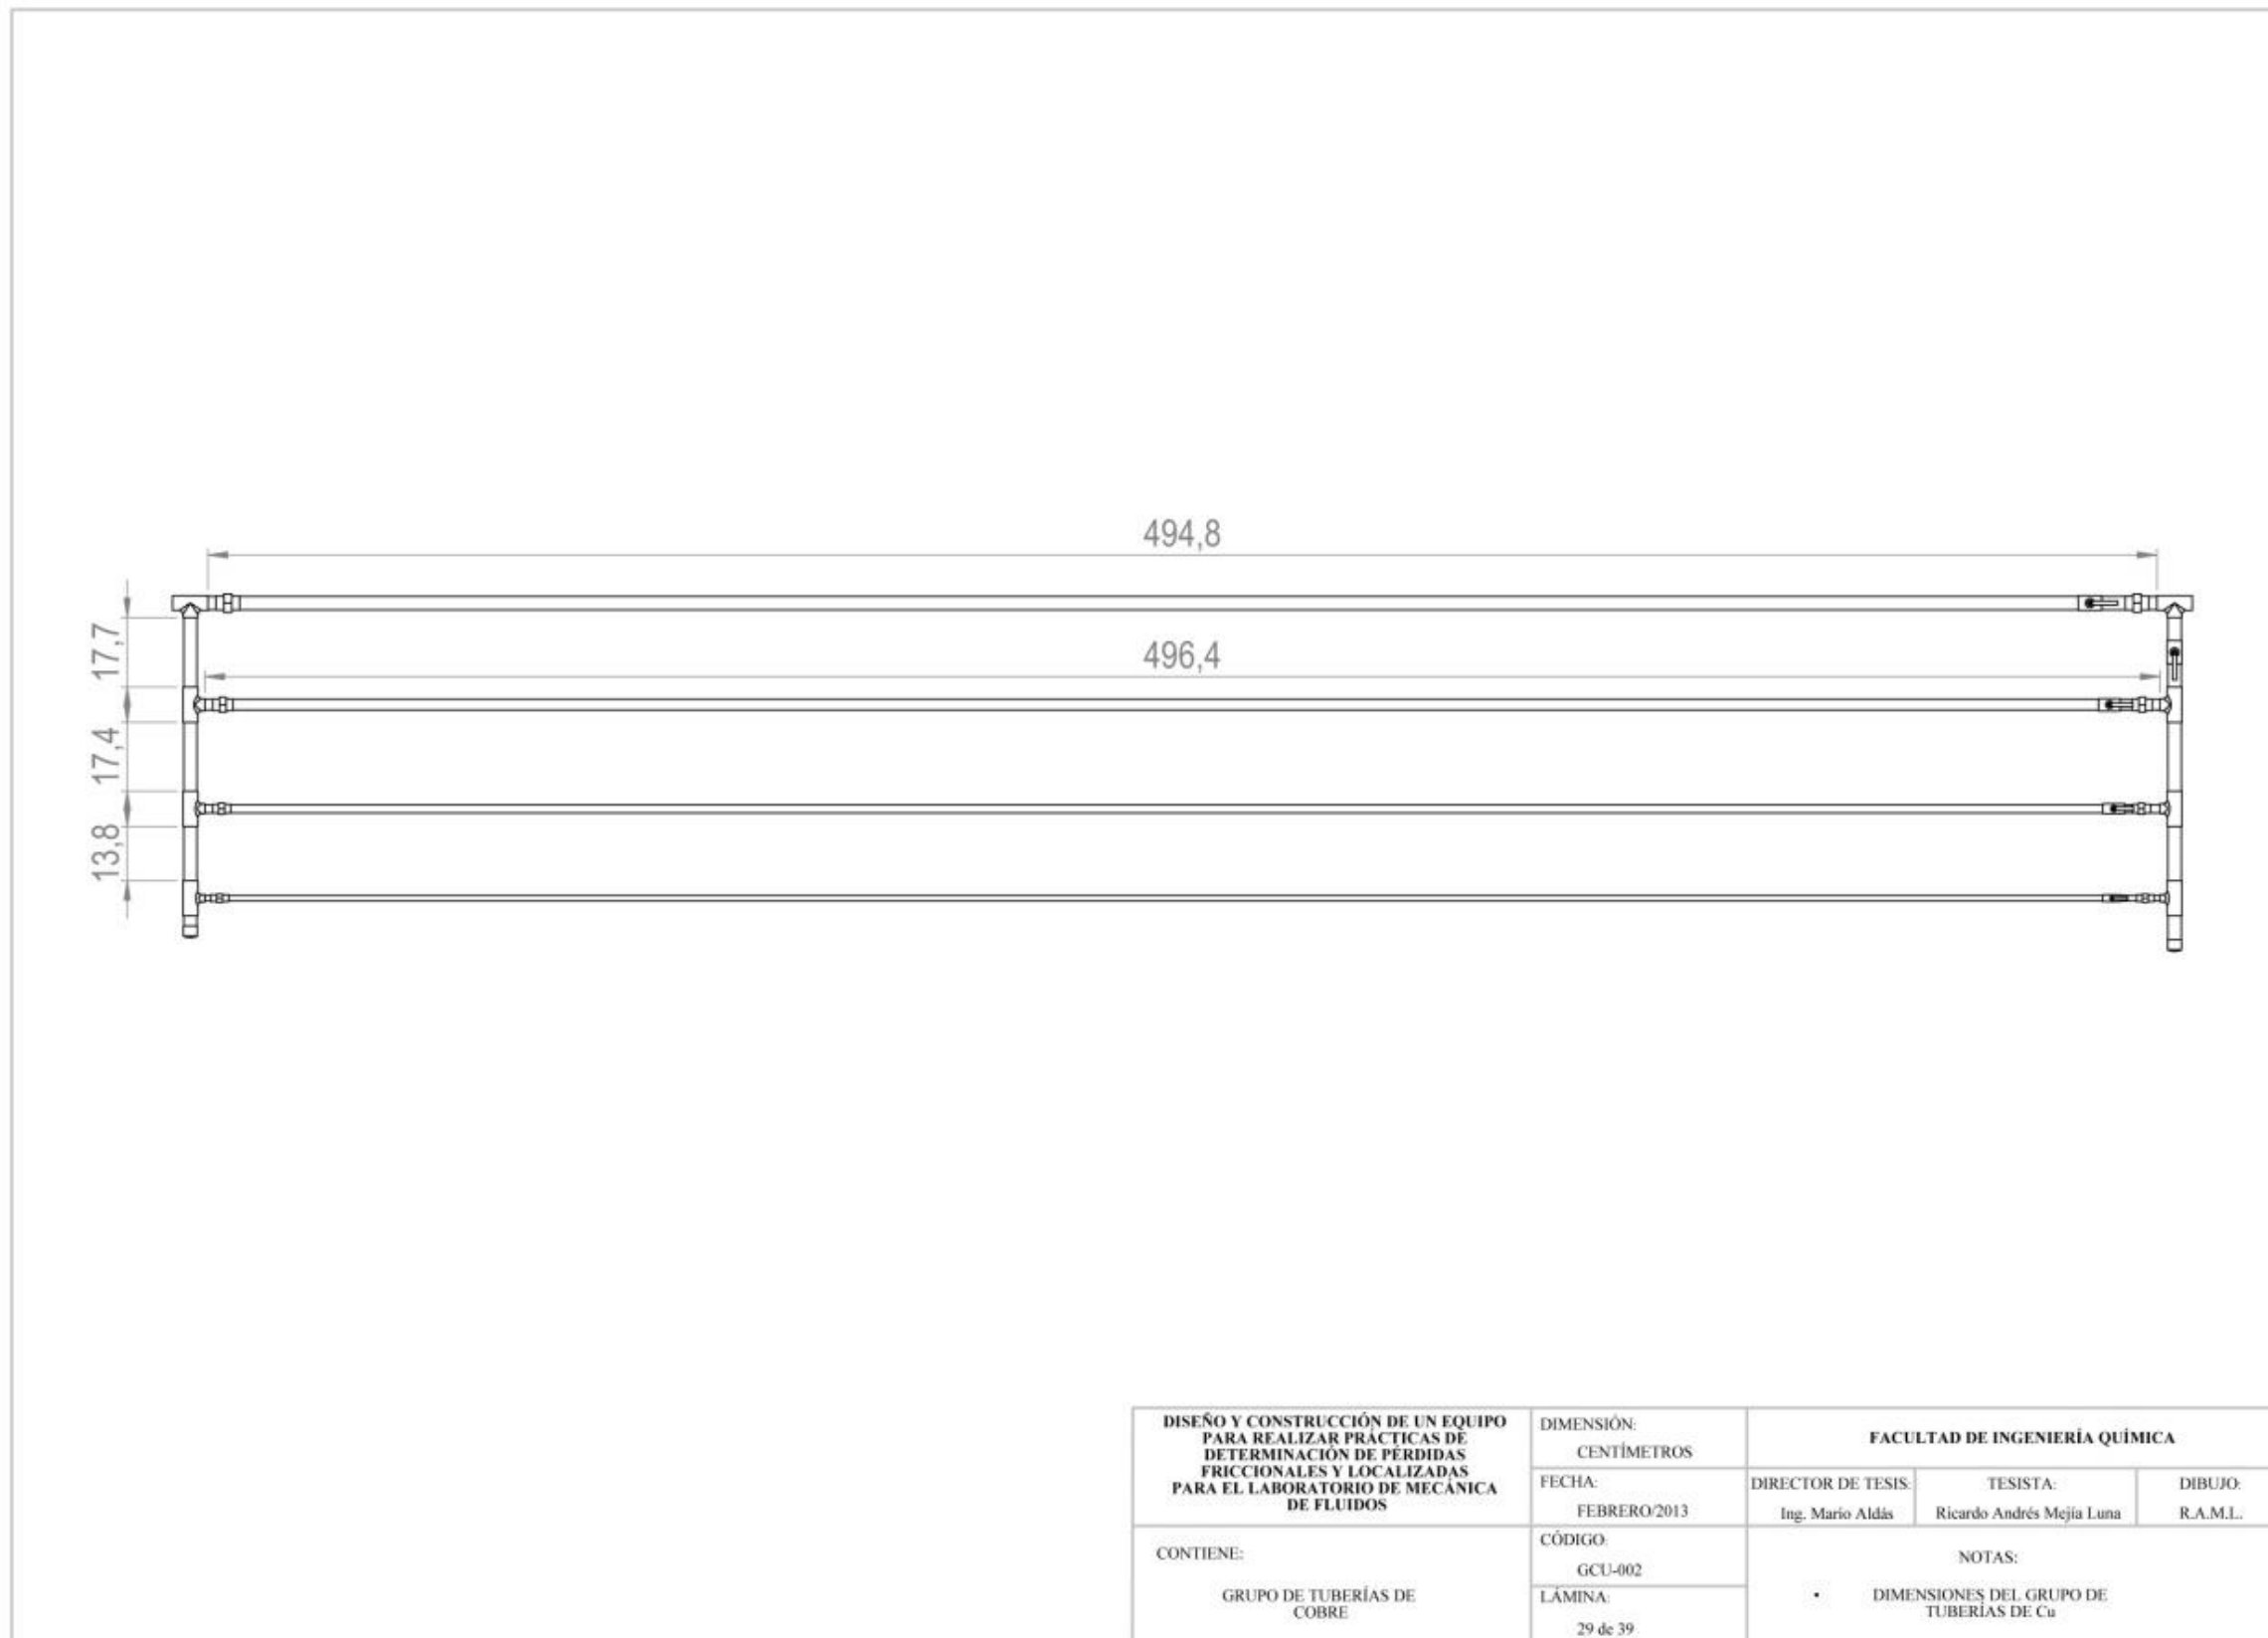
Dimensiones del grupo de tuberías de Cu
